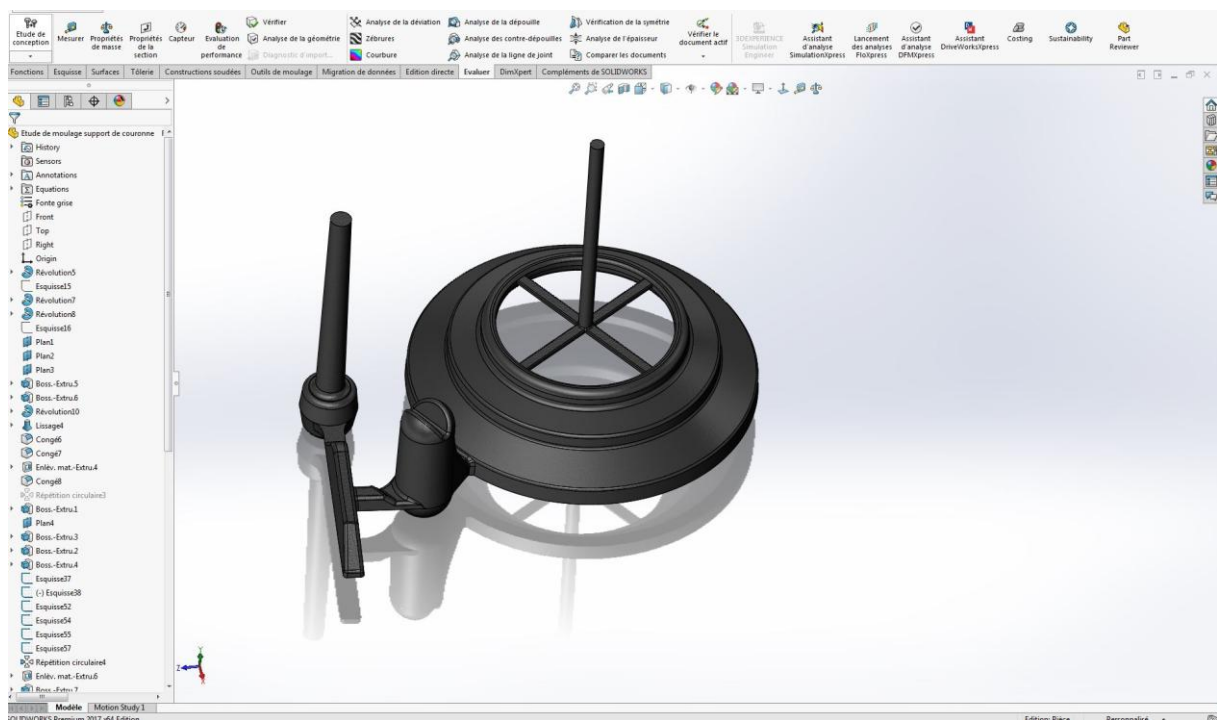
Dessin de support de couronne ABS par le SolidWorks
